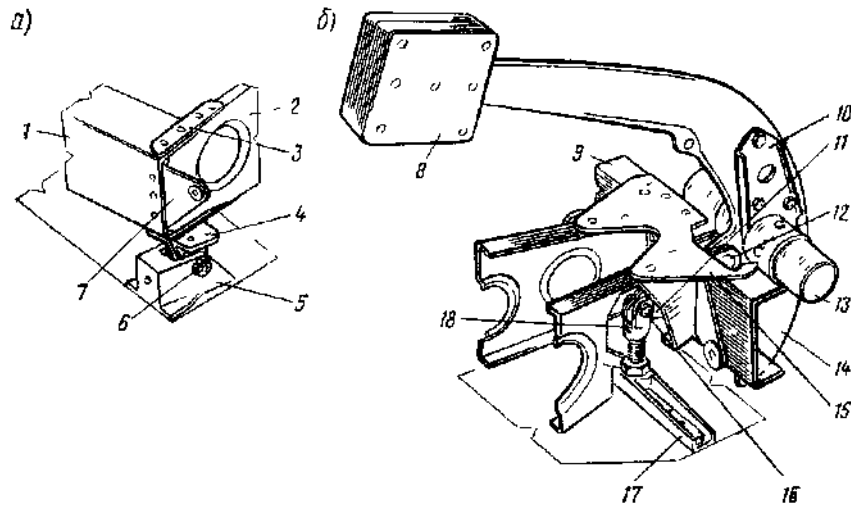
Узлы крепления стабилизатора и руля высоты:
